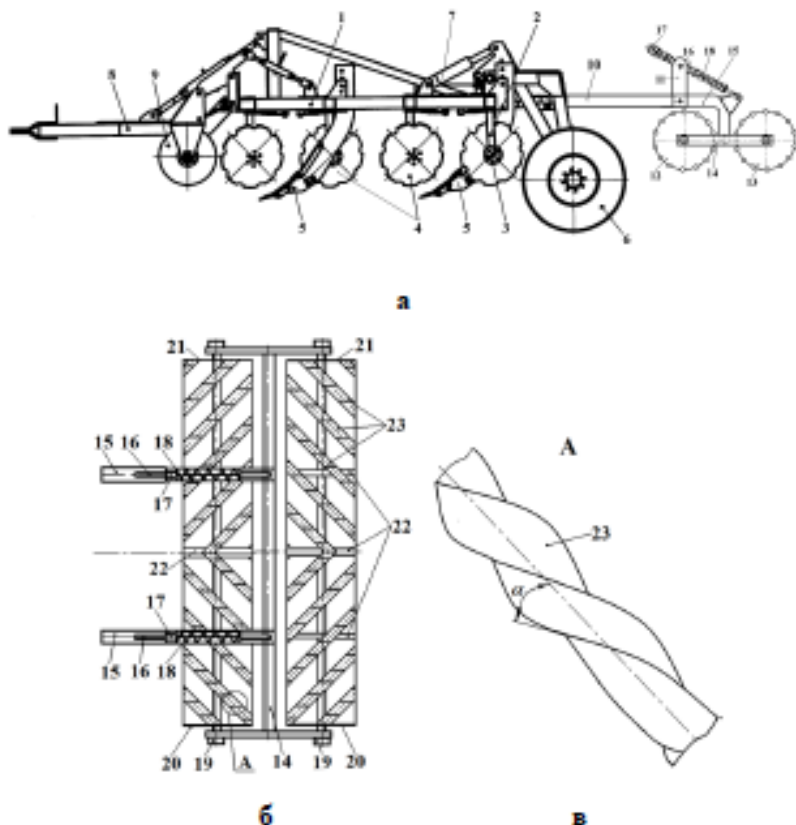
Комбинированный почвообрабатывающий агрегат:
